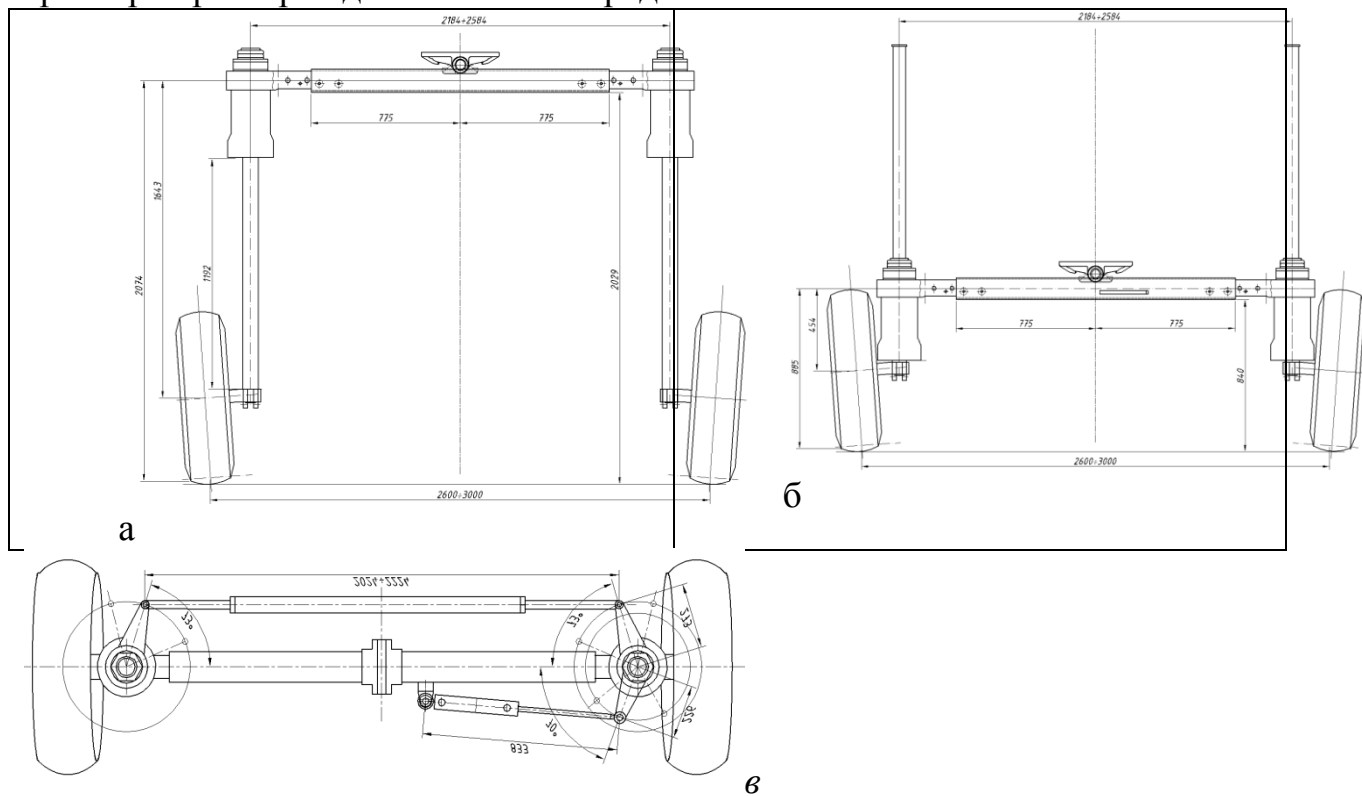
Рулевой механизм: а- вид спереди высококлиренсное положение; б- вид спереди низкоклиренсное положение; в- вид сверху.
